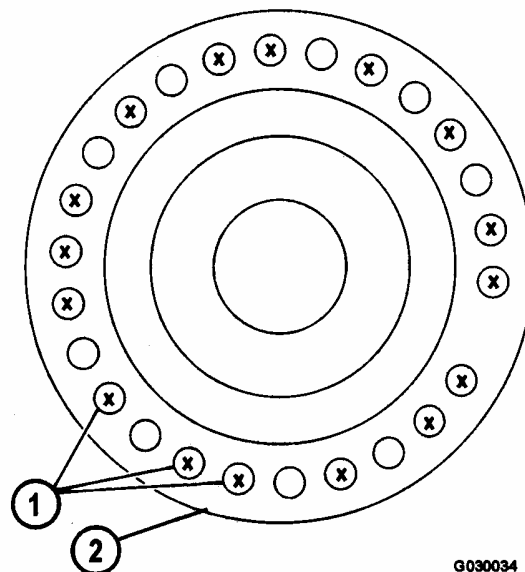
HERRAMIENTA DE DESMONTAJE DEL HUSILLO
